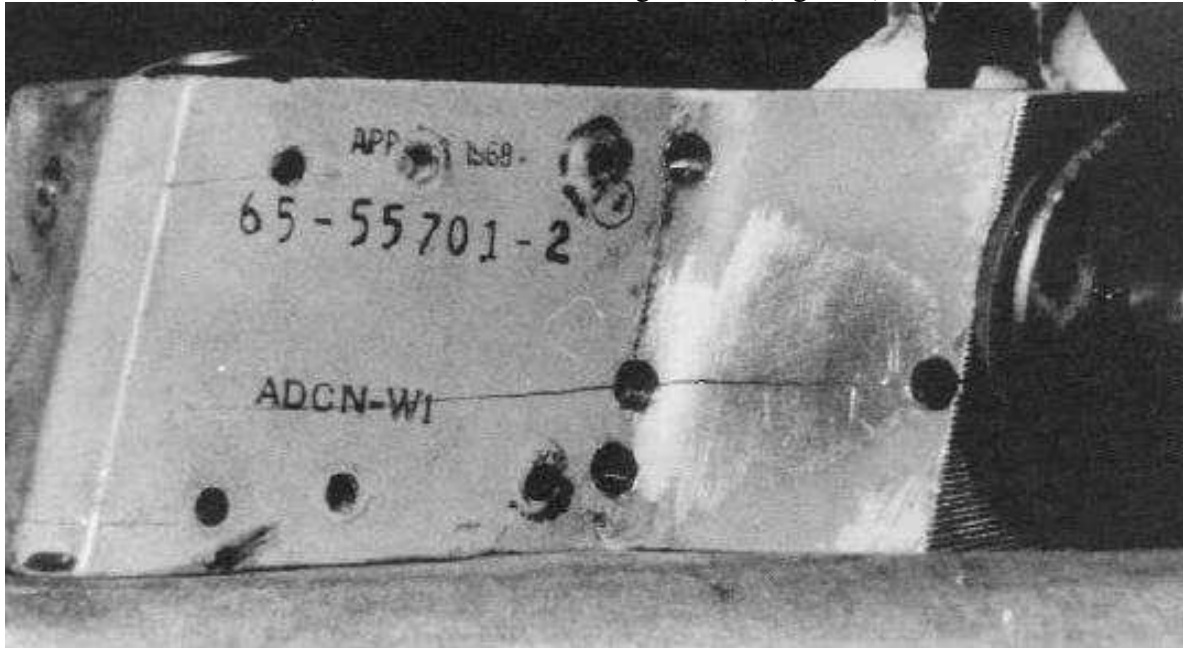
Corrosão sob tensão fraturante (SCC) em um componente de liga de alumínio 7079-T6.
